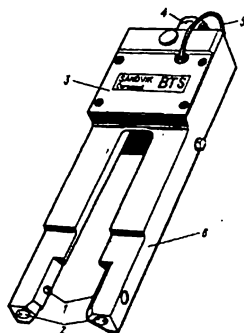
Загальний вигляд захвата для заміни інструментальних блоків:
